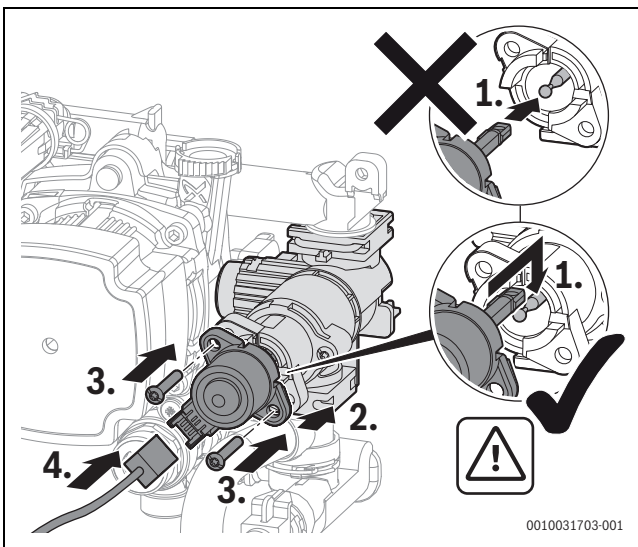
Motor am 3-Wege-Ventil einbauen (Variante mit Schrauben)
